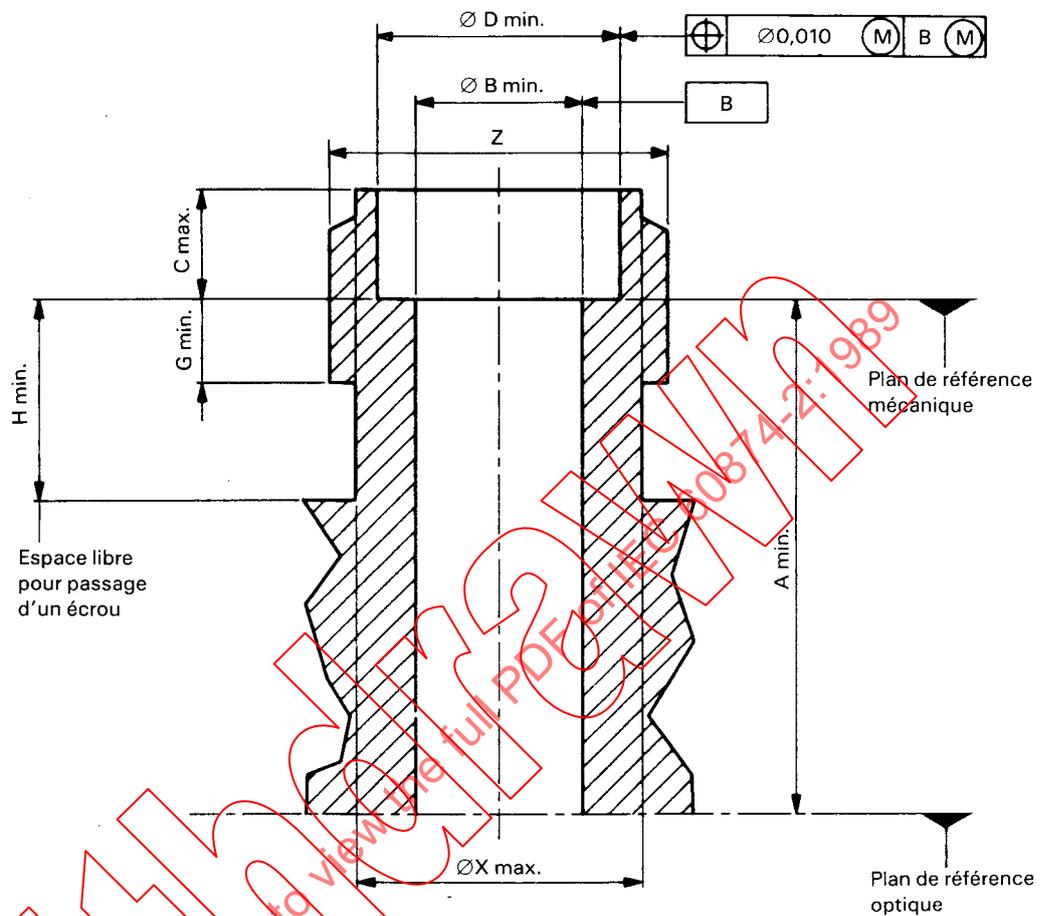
Raccord (pour les dimensions voir tableau 2)
